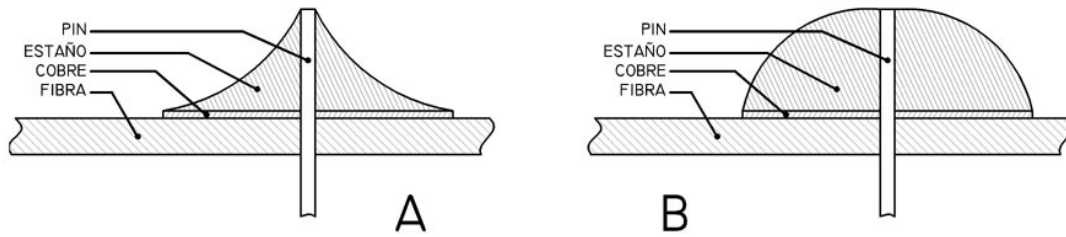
Soldadura correcta (A) i soldadura incorrecta (B)
